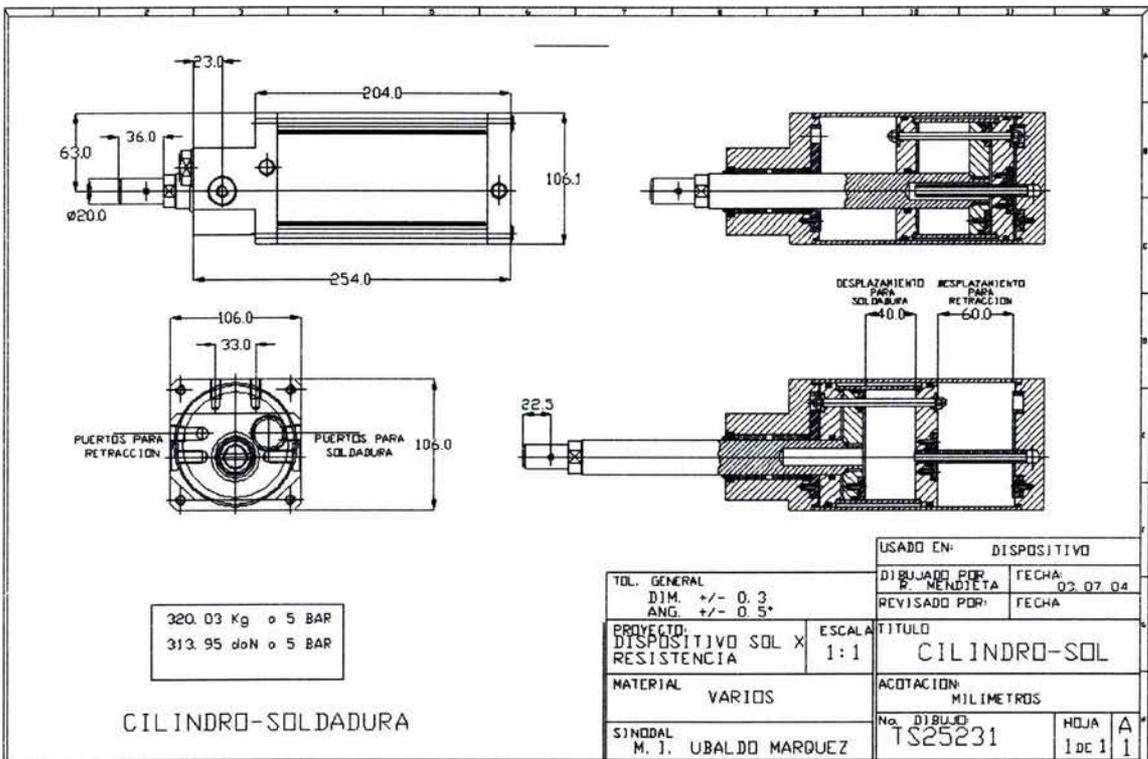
Cilindro para soldadura por resistencia.
